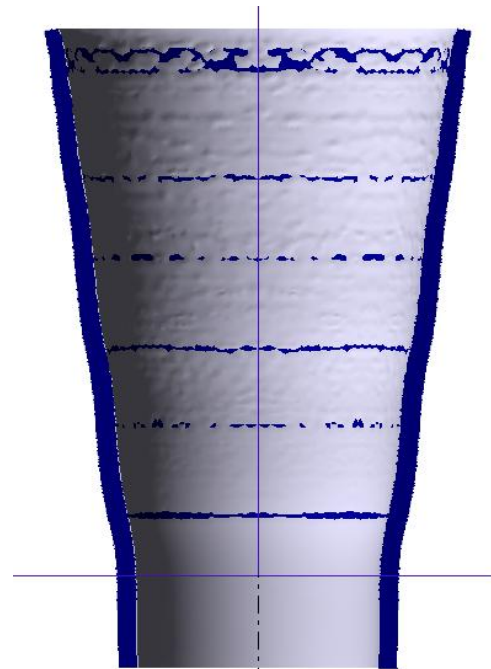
Схема контакта рабочей поверхности пуансона с заготовкой
